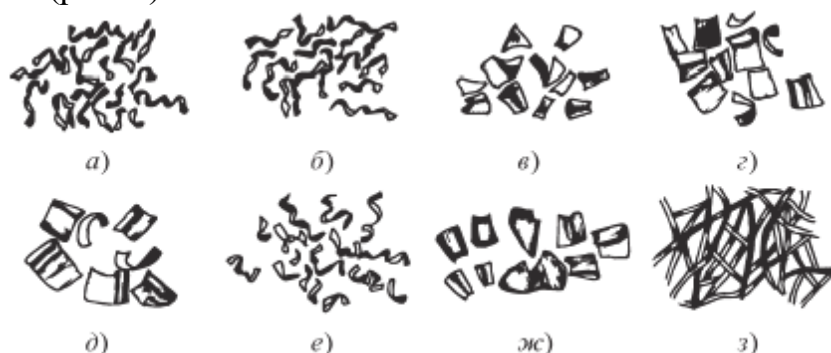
Оптимальная форма стружки при обработке глубоких отверстий инструментами с определенностью базирования: а — ружейными сверлами; б — кольцевыми сверлами с наружным отводом стружки; в — сверлами БТА; г — кольцевыми сверлами БТА; д — расточными головками БТА; е — плавающими двухлезвийными расточными блоками; ж — эжекторными сверлами; з — недопустимая форма стружки
